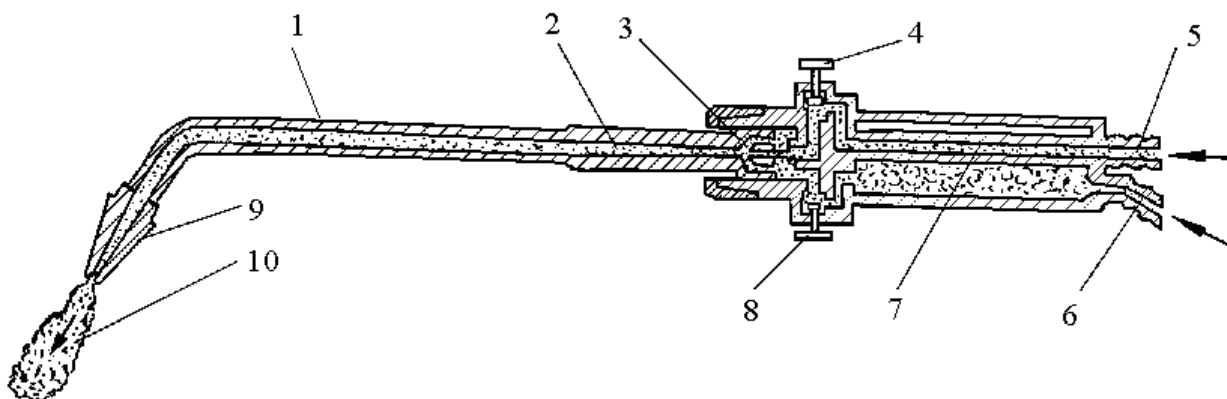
Схема зварювального пальника: 1 – трубка; 2 – камера змішування; 3 – інжектор; 4 – вентиль для регулювання; 5 – ніпель для підводу кисня; 6 – ніпель для підводу горючого газу; 7 – трубка; 8 – вентиль для регулювання; 9 – мундштук; 10 – зварювальне полум'я
